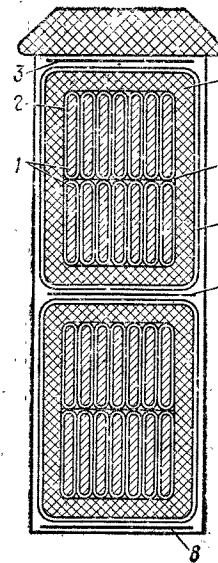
Изоляция пазовой части проводников тягового двигателя со стороны коллектора
